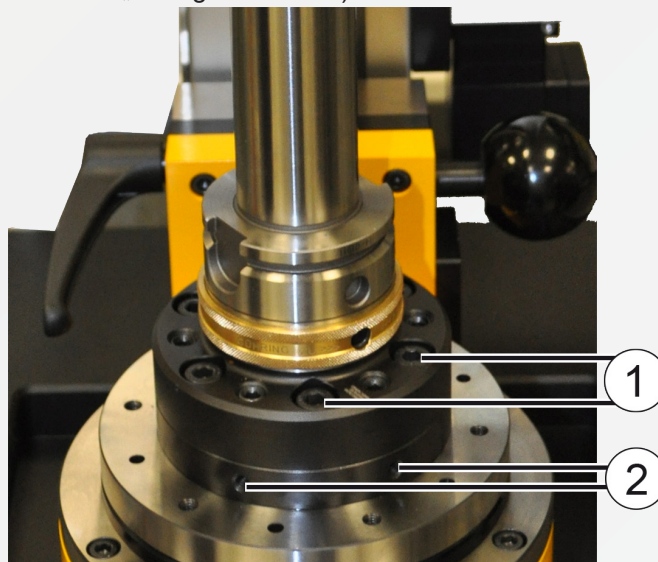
Befestigungsschrauben (1) bzw. Justierschrauben (2)
